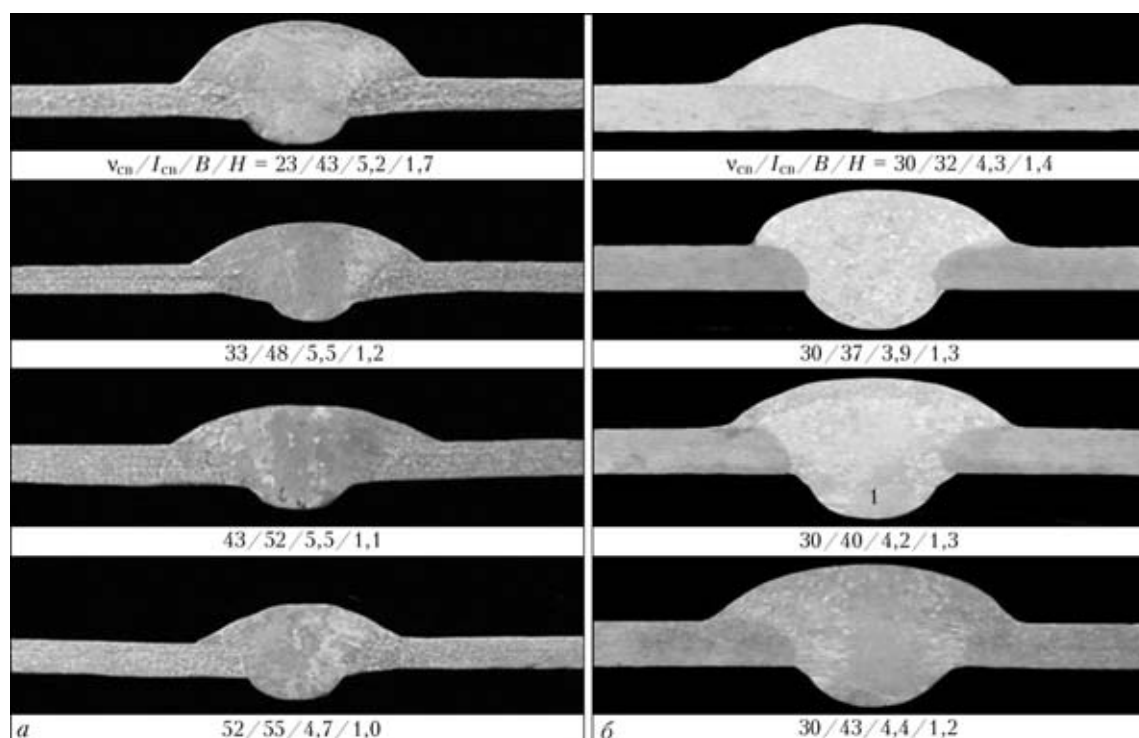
Влияние режима сварки на геометрию соединений сплава АМц (а) и АМг2 (б) толщиной 1 мм. Здесь и далее номер в области металла шва соответствует номеру опытной сварки с погонной энергией согласно рис. 3
